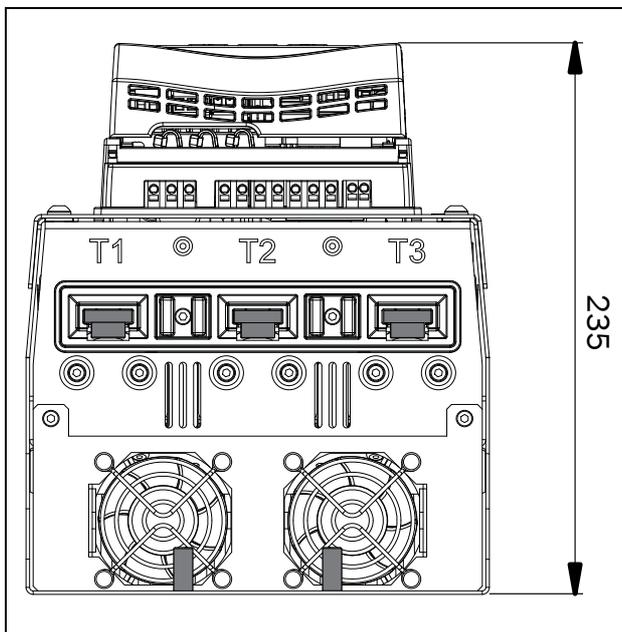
Габаритные размеры Emotron TSA типоразмера 3, вид снизу.
